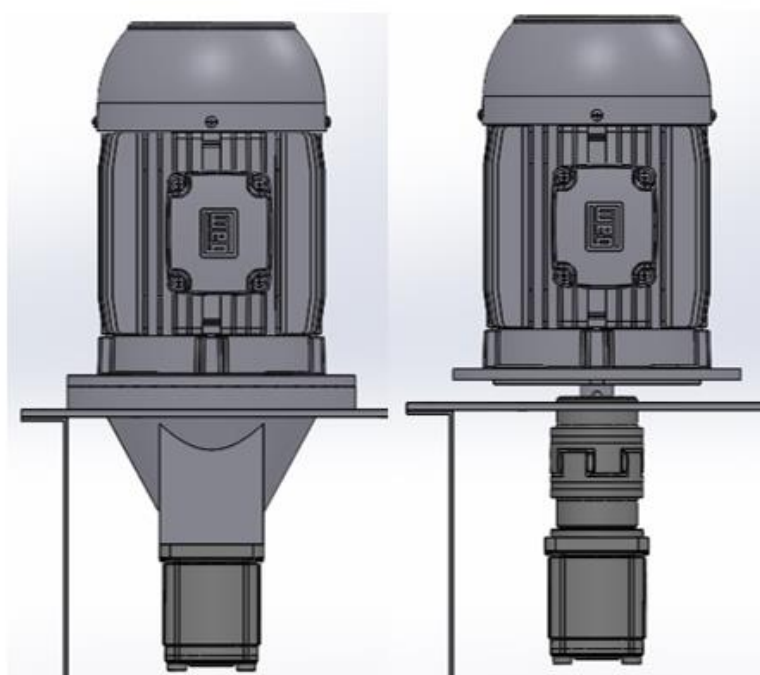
Montagem motor e bomba acoplada (imagem direita com a flange oculta) - Fonte: Autor
